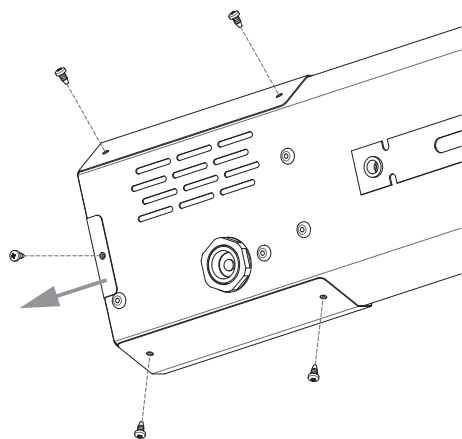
Снятие боковой крышки обогревателя для доступа к распределительной коробке.
